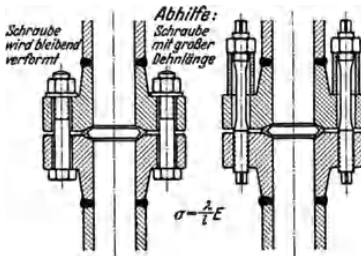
Hochdruckflanschverbindung. Schrauben mit großer Dehnlänge zur Aufnahme der aufgezogenen Verformung durch ungleichmäßige Wärmedehnung von Flansch und Schrauben.
